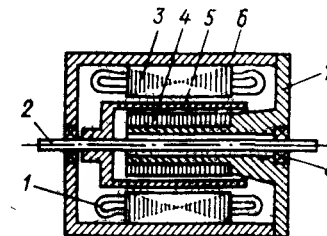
Конструктивная схема управляемого двигателя с полым немагнитным ротором: 1 — обмотка; 2 — вал; 3 — внешний магнитопровод; 4 — внутренний магнитопровод; 5 — полый немагнитный ротор; 6 — корпус; 7 — крышка; 8 — подшипник
